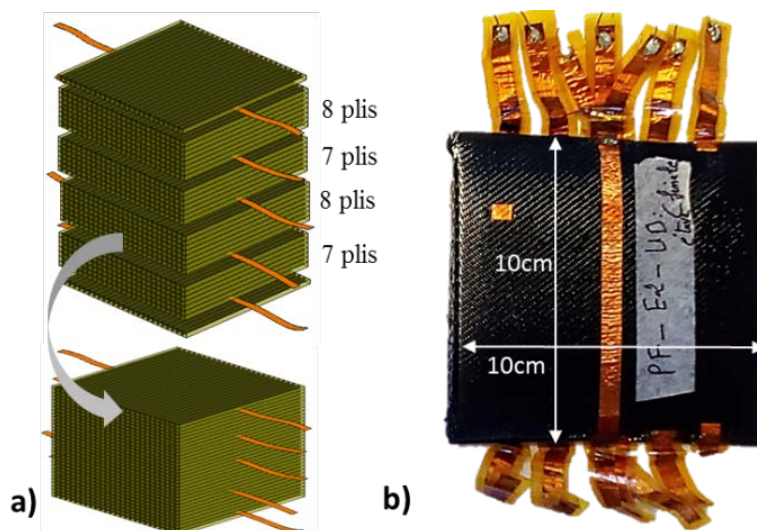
a) le plan et b) la photo de la plateforme d'instrumentation transversale inter-ply (32 plis)
